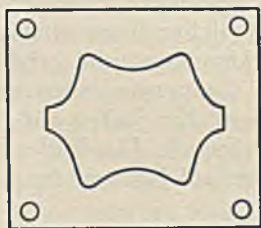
Schlauchmaschinenkapsel für ebene Lauffläche
